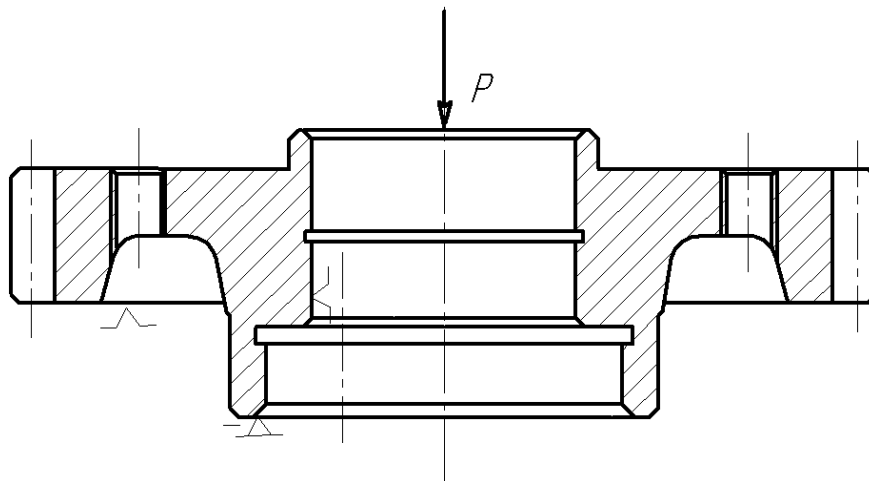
Схема установки Колесо зубчасте НПО 639.00.004
